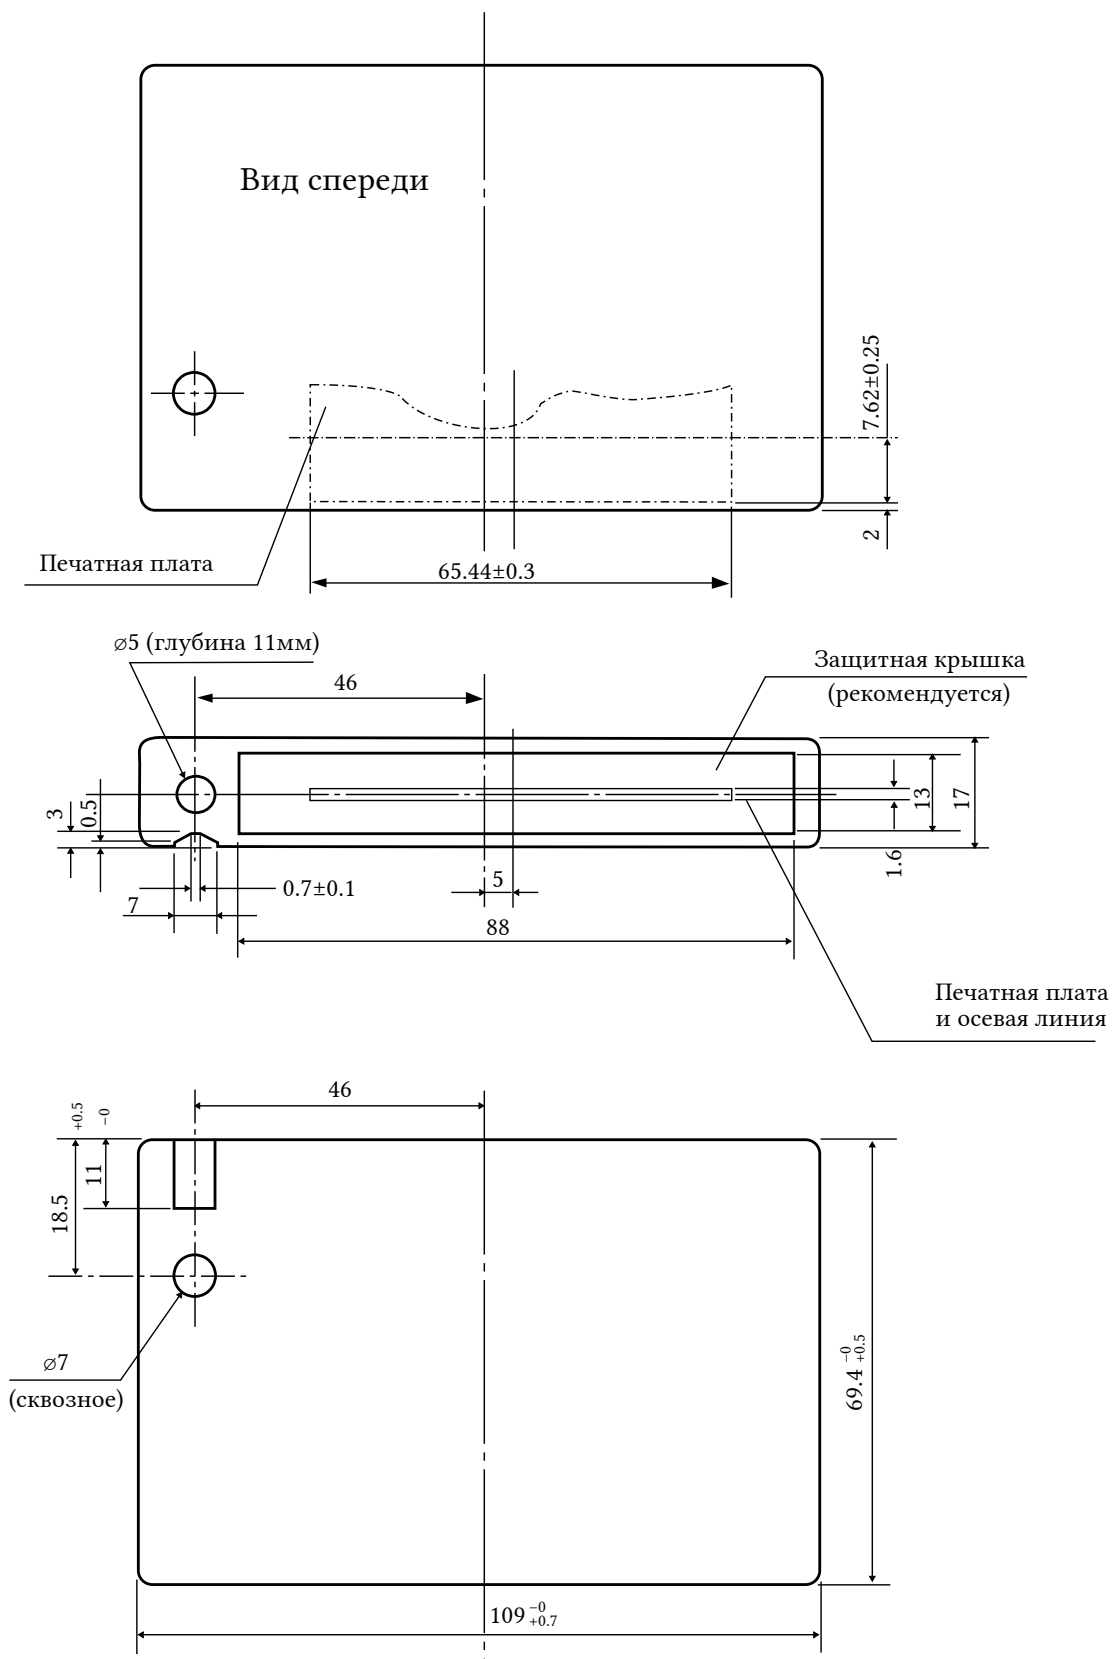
Геометрические размеры корпуса стандартного картриджа MSX.
